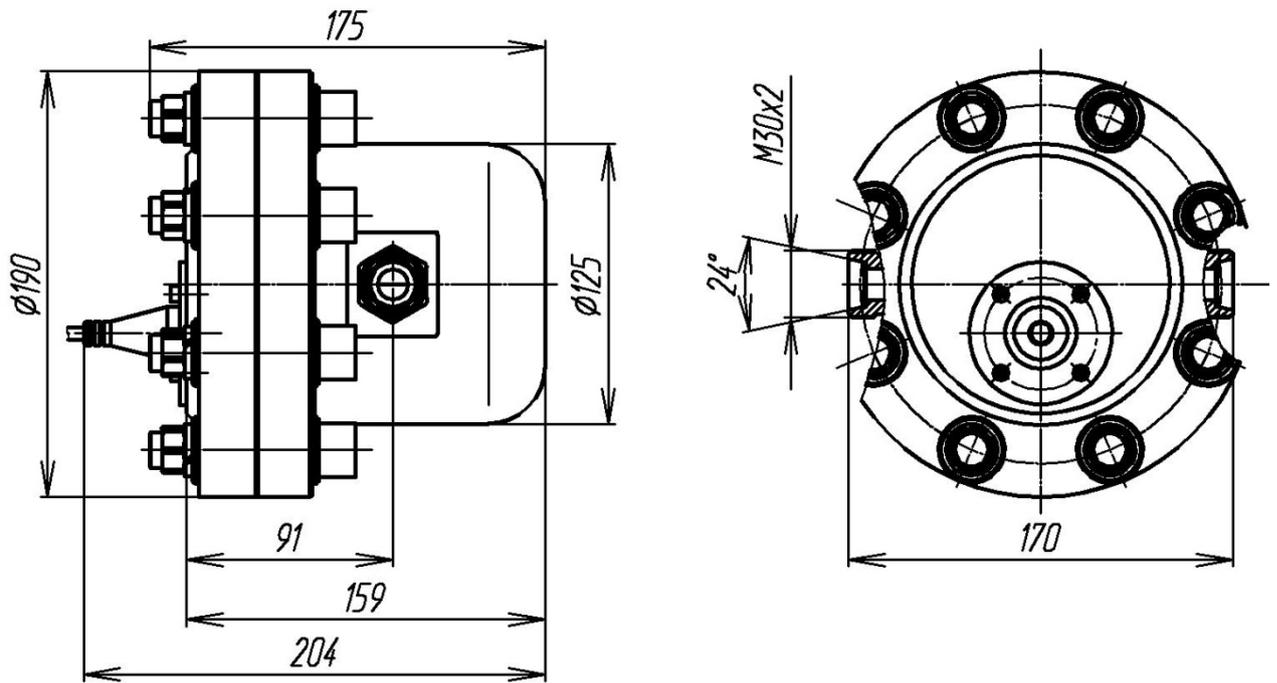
Габаритные и присоединительные размеры расходомера-счётчика RVШ-PL-020-250-Z-xx
